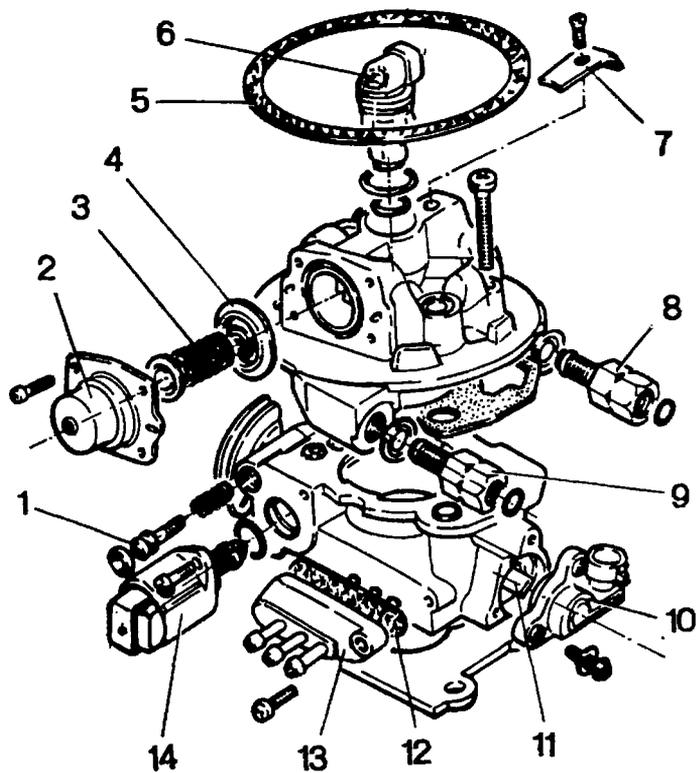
Детали и узлы агрегата центрального впрыска: 1 - винт заводской регулировки холостого хода; 2 - крышка регулятора давления топлива; 3 - пружина регулятора; 4 - диафрагма регулятора; 5 - прокладка воздушного фильтра; 6 - форсунка; 7 - держатель форсунки; 8 - штуцер подвода топлива; 9 - штуцер отвода топлива; 10 - датчик положения дроссельной заслонки; 11 - ось дроссельной заслонки; 12 - прокладка патрубков; 13 - корпус патрубков для отбора разрежения; 14 - регулятор холостого хода
